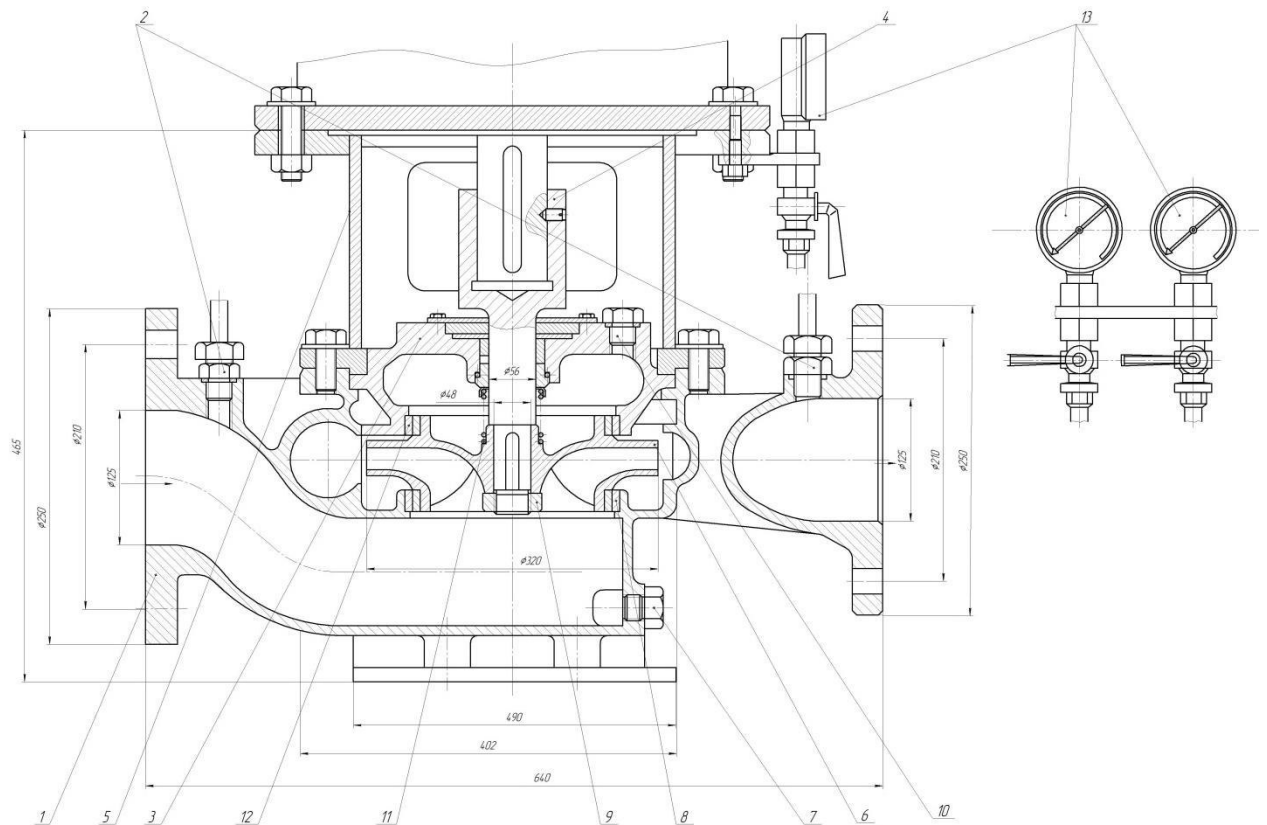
Конструктивні елементи суднового відцентрового насоса типу B125 VIC: 1 — спіральний корпус (равлик); 2 — штуцери для підключення манометрів; 3 — корпус механічного ущільнення; 4 — з'єднувальна муфта; 5 — захисний кожух; 6 — робоче колесо (крильчатка); 7 — дренажна зливна пробка; 8 — переднє компенсаційне (щілинне) кільце; 9 — гайка кріплення крильчатки; 10 — фіксуючий гвинт; 11 — пружина
